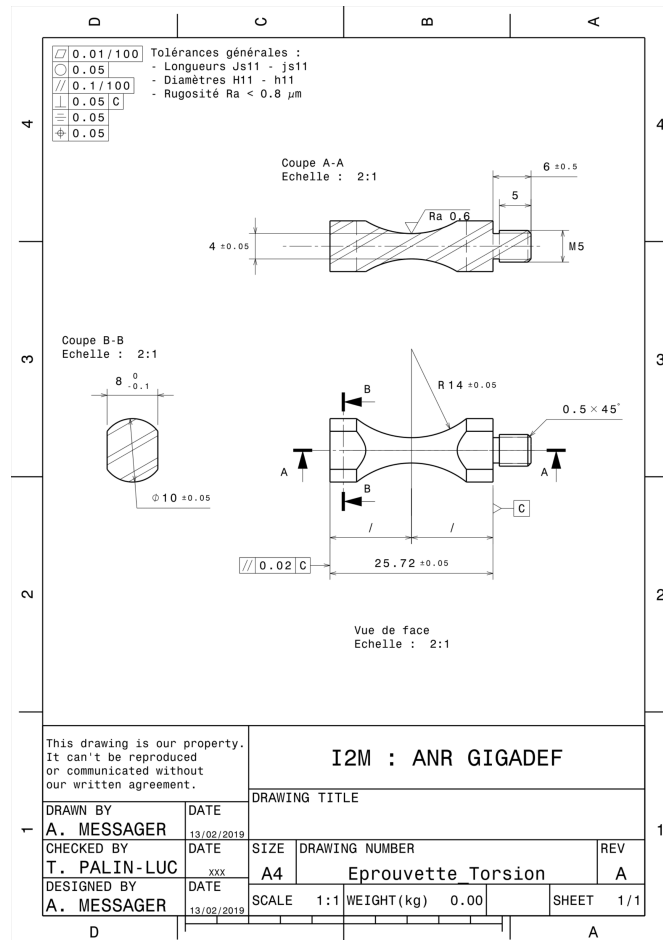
Dessin de définition des éprouvettes d'essais de torsion ultrasonique
